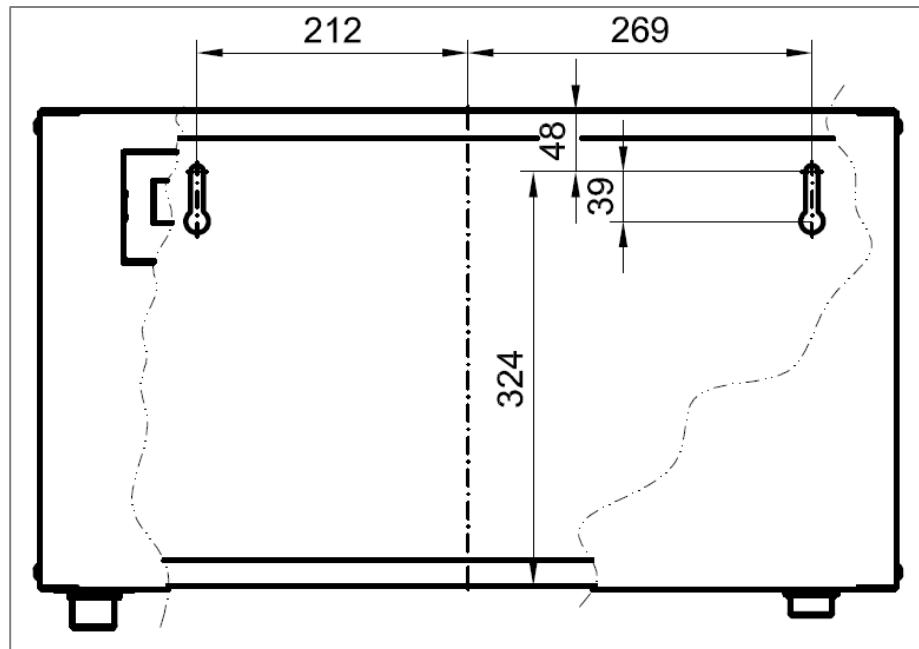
Schéma de perçage pour la fixation au mur du chauffe-eau instantané
